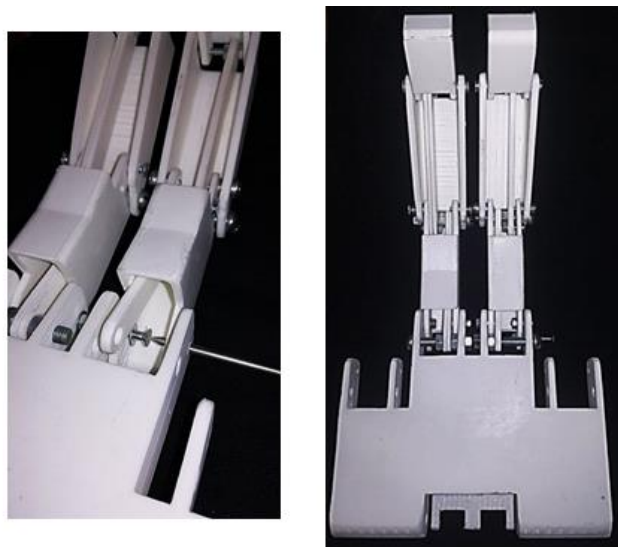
Proceso de montaje de los dedos mediante las piezas fabricadas en la impresora 3D
